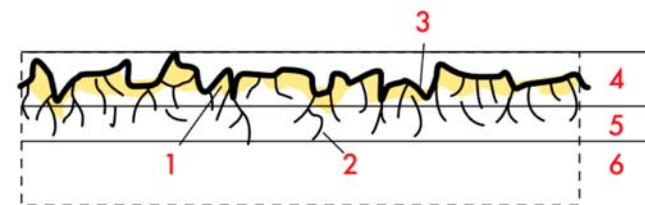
Поперечное сечение отшлифованной пластины: 1 — зона неупругой деформации; 2 — микротрещины; 3 — поверхность после шлифовки; 4 — рельефный слой (0,5—1,0 мкм); 5 — приповерхностный слой (1,0—2,0 мкм); 6 — основной материал [7]
